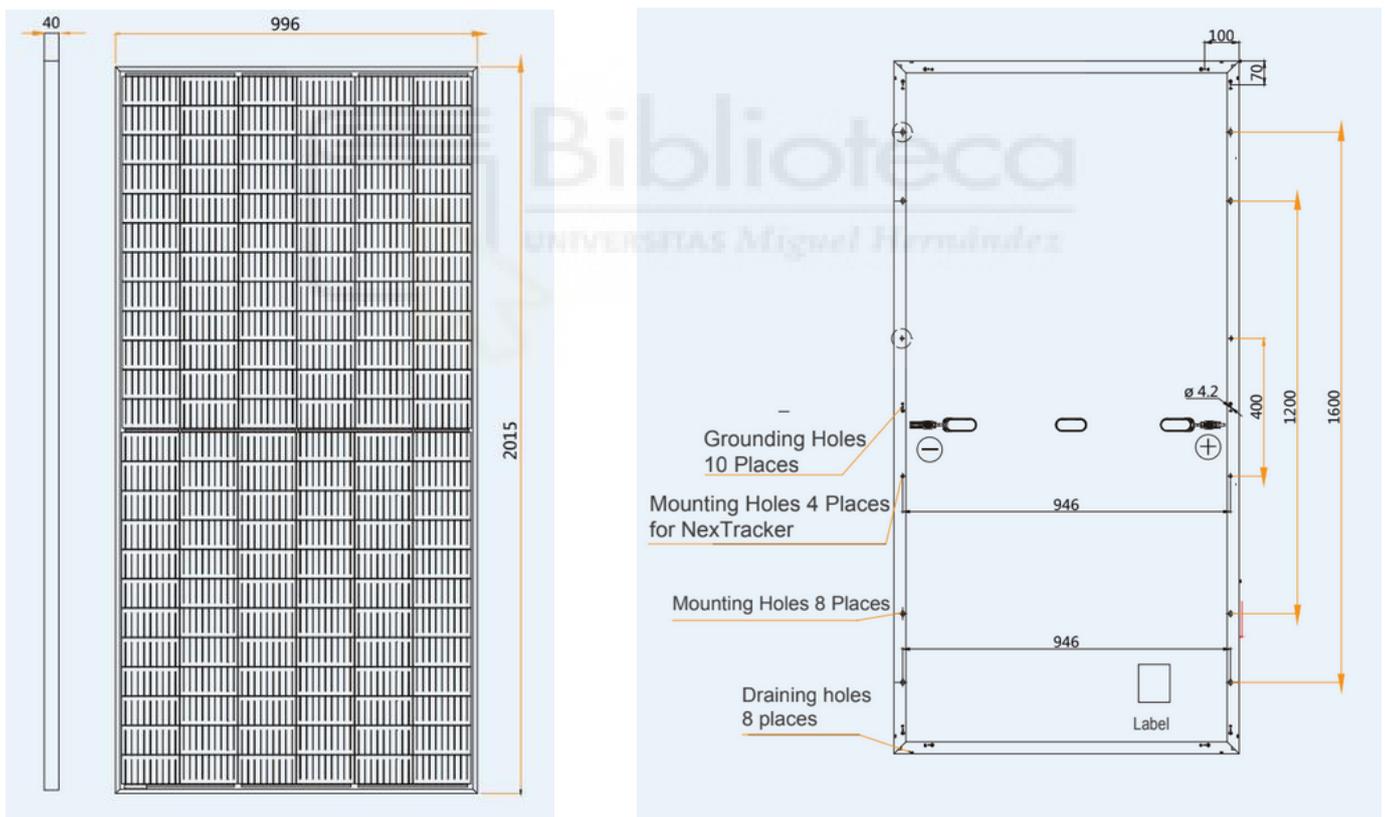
Dimensiones del módulo fotovoltaico, a la izquierda, parte delantera, y a la derecha, parte trasera [mm] [37]
